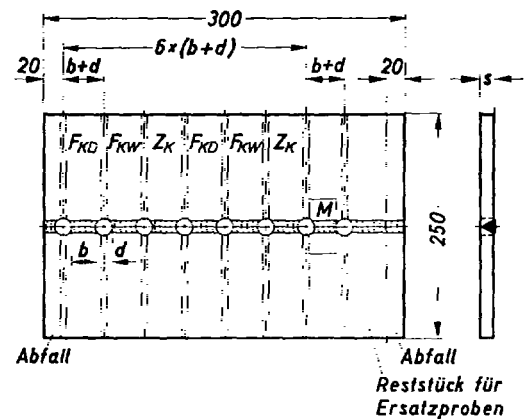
Stumpfnahtrprüfstück für Blechschweißer an $s \geq 4$ mm (Probenlage schematisch eingezeichnet)
